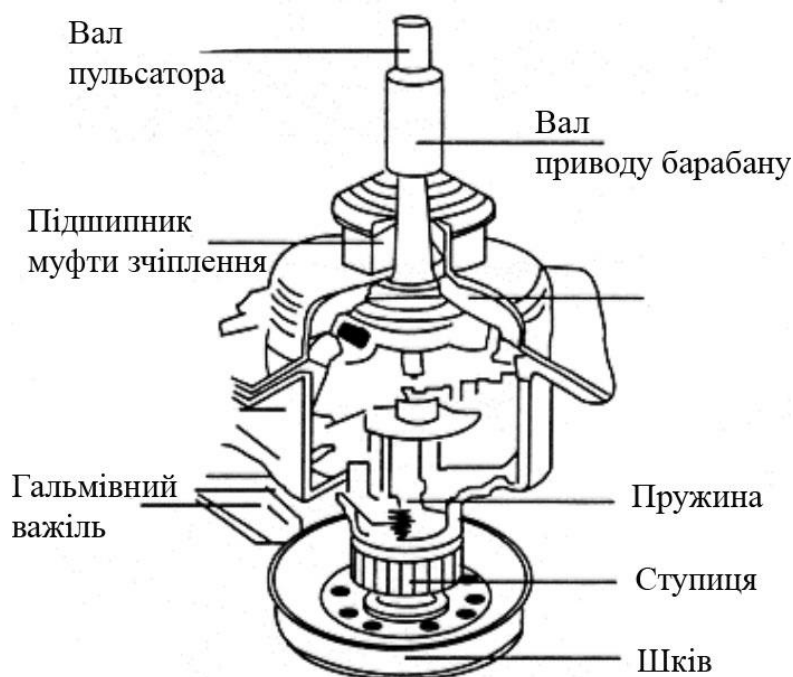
Пристрій механізму передачі (редуктора)
